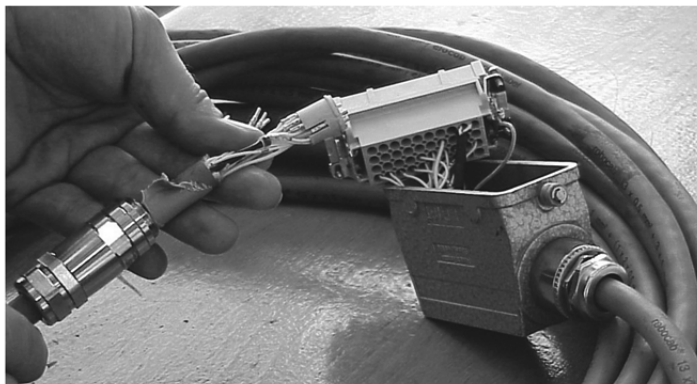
Schweißleitung; zwei Typen von Steckern
